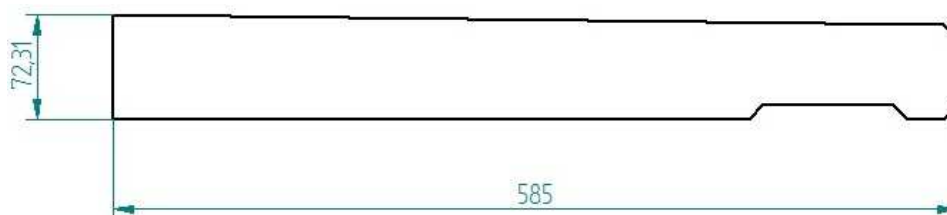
Sección de la placa de remate (dimensiones en mm)
